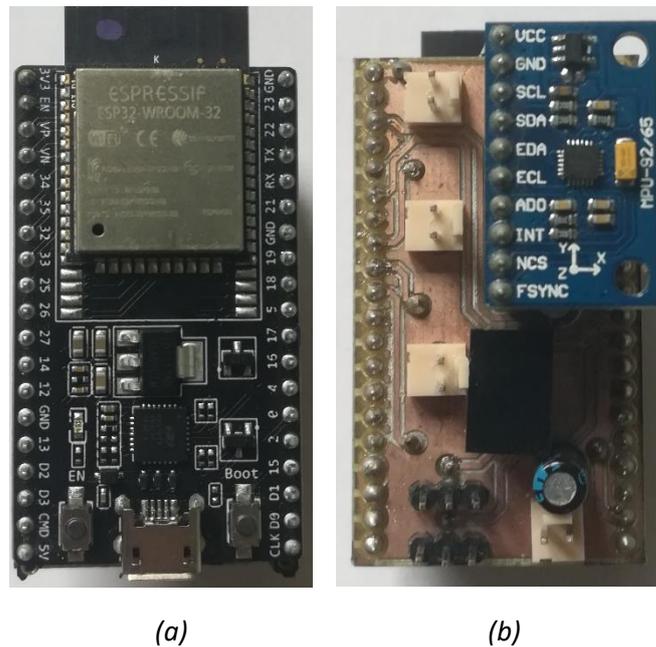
(a) Cara Top módulo montado (b) Cara Bottom módulo montado
